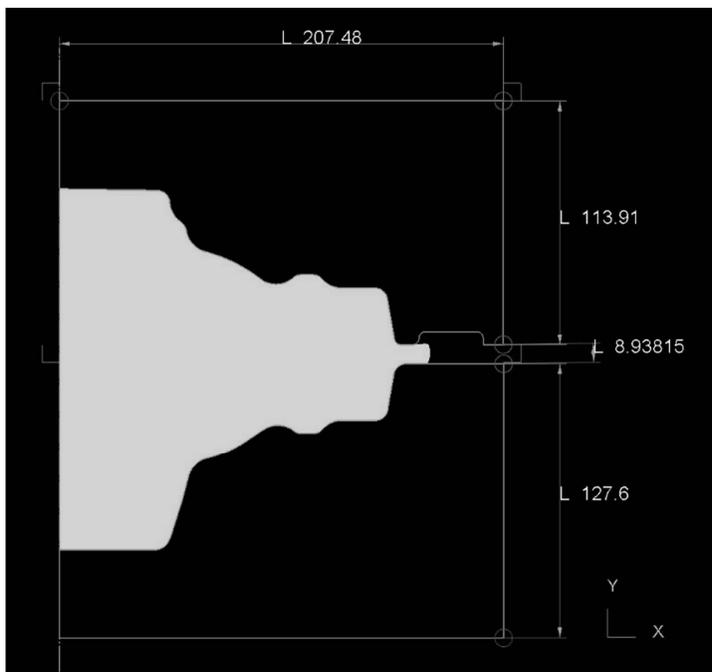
Формообразующая геометрия поверхностей инструмента штамповочных
